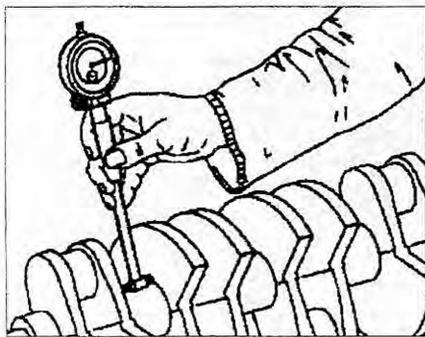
Измерение ширины коренной шейки коленчатого вала.
